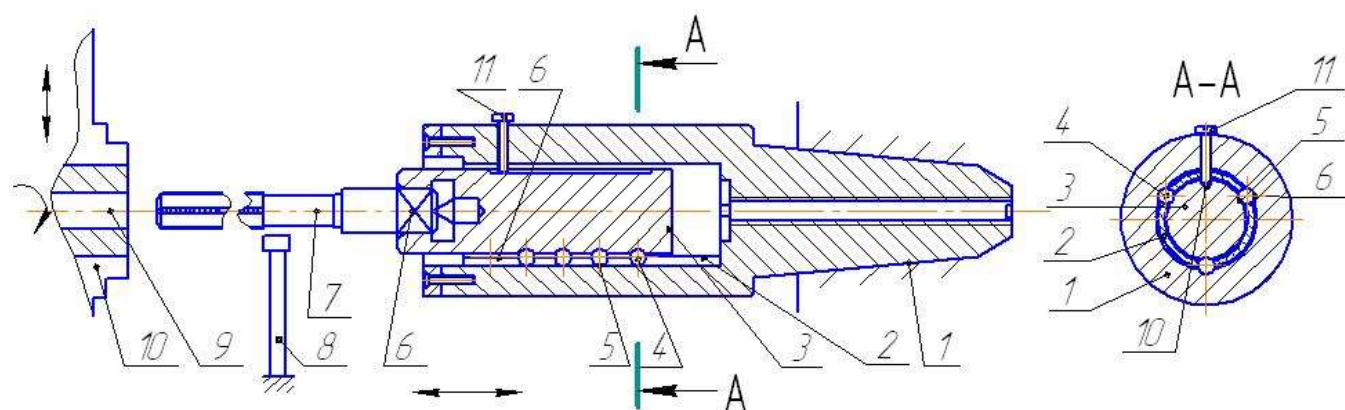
Патрон для нарізання різі в корпусних деталях (Патент № 51876
